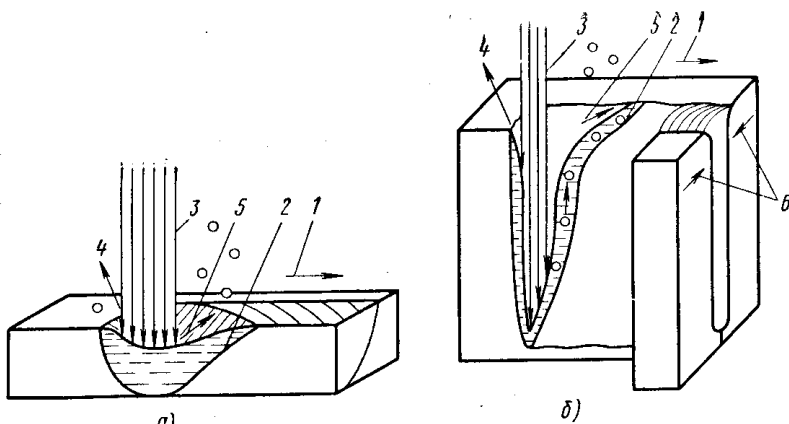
Схема электронно-лучевой сварки металлов малой (а) и большой (б) толщины:
